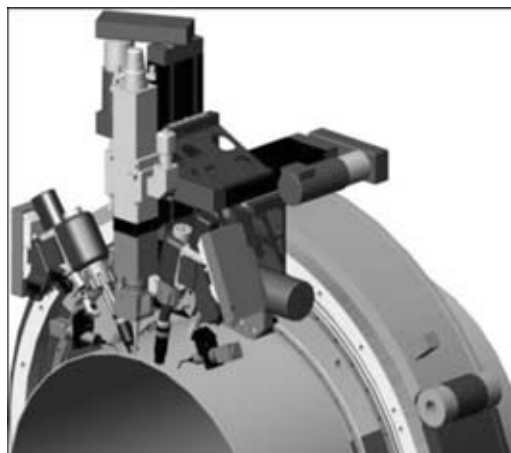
Проектный вариант оборудования для гибридной сварки труб усовершенствованной поворотной конструкции
